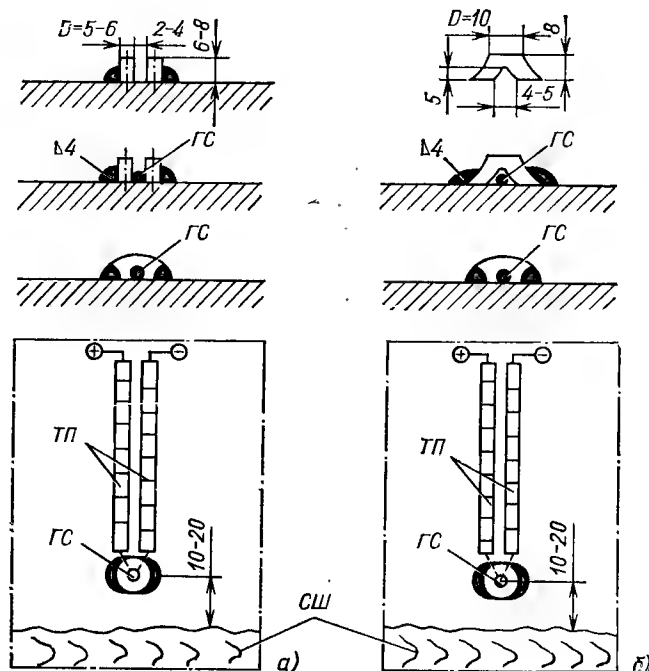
Схема крепления горячего спая ГС термопары ТП к поверхности нагреваемого сварного изделия.
